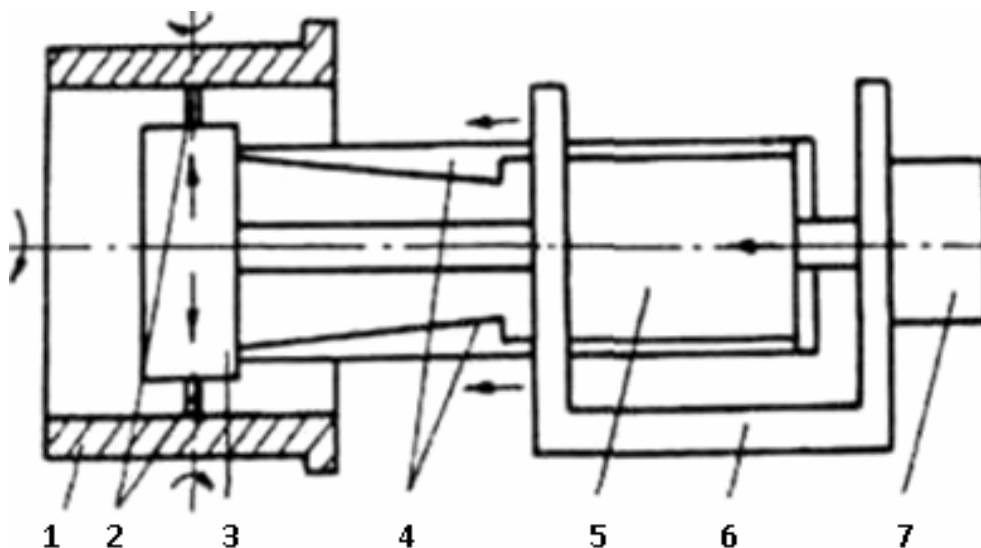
Схема устройства для латунирования гильз цилиндров
